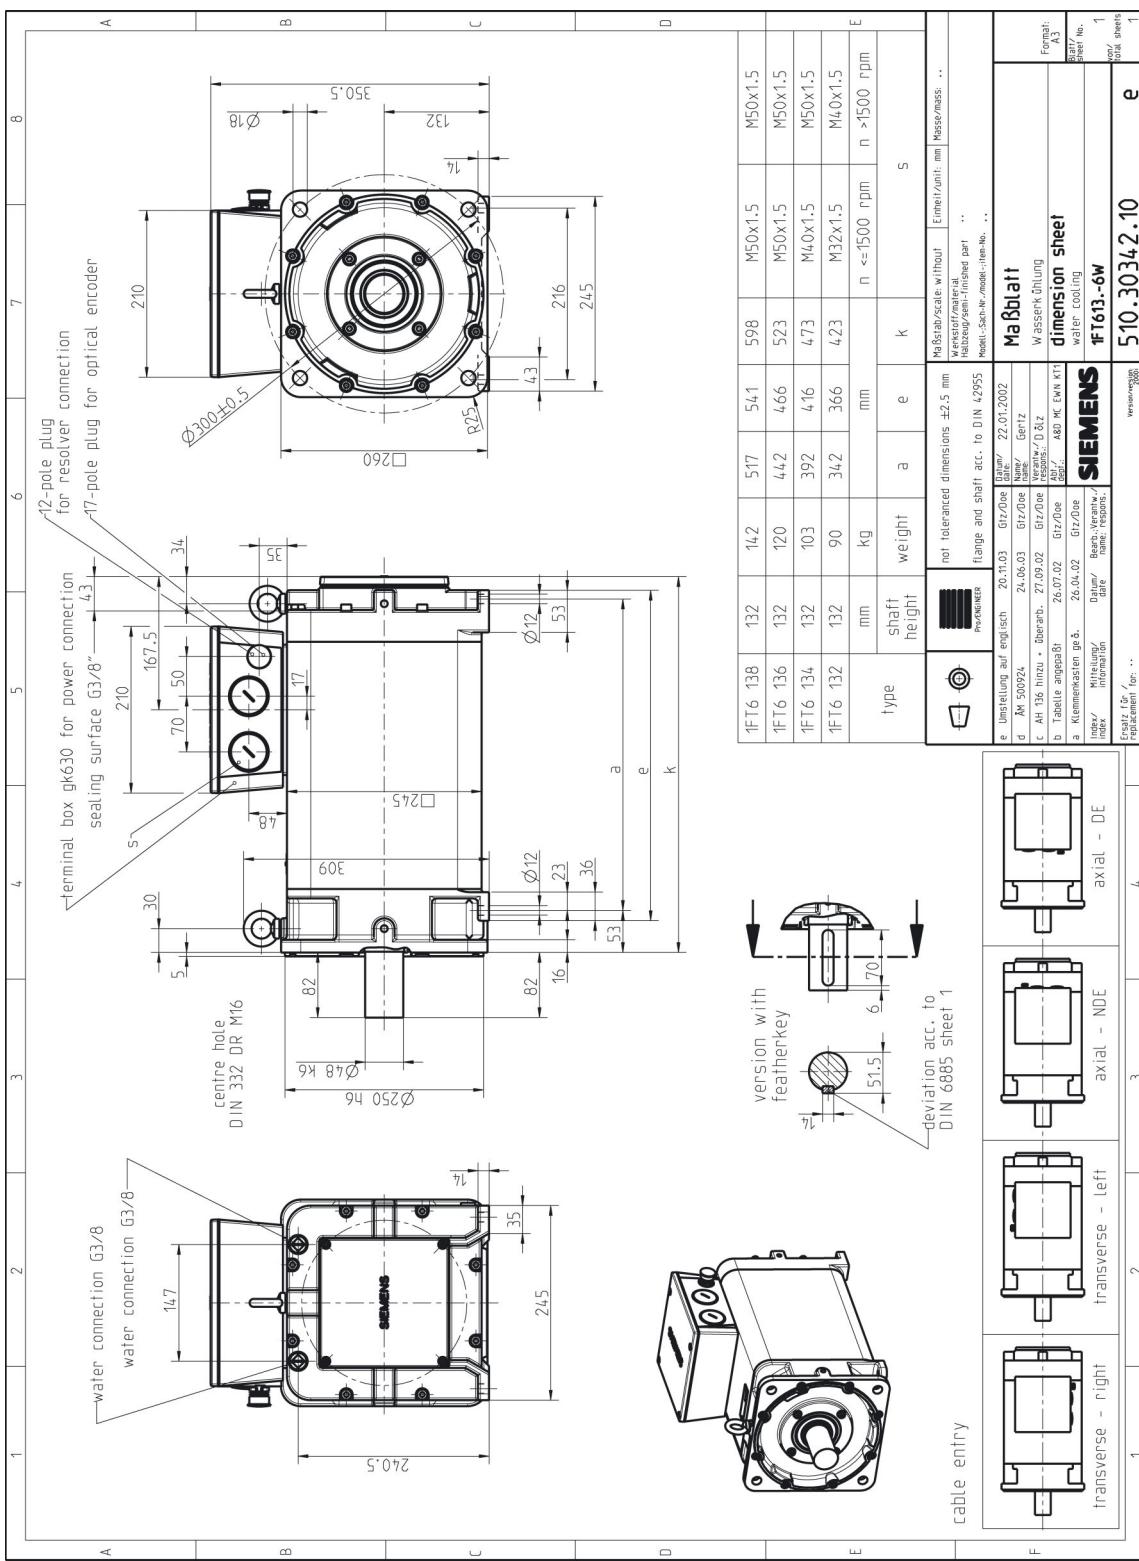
1FT613□ wassergekühlt mit Klemmenkasten
